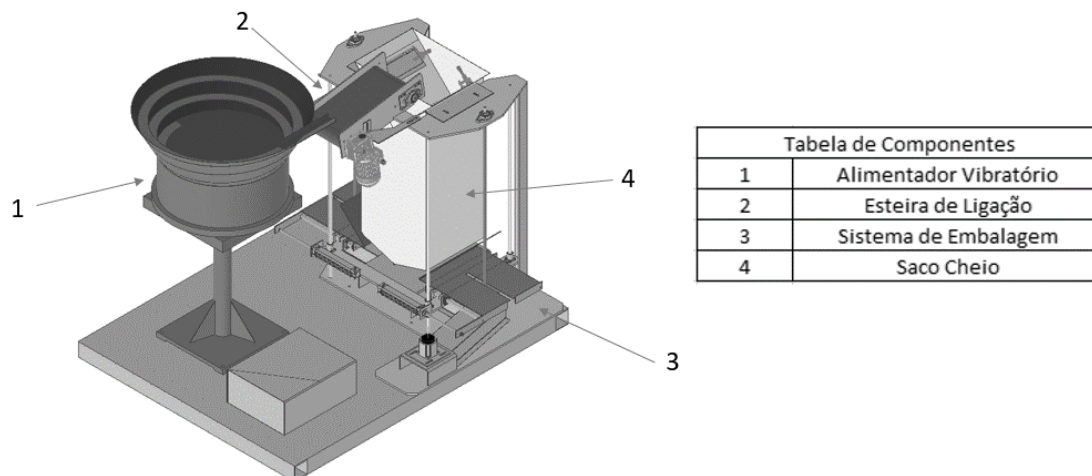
Representação CAD 3D da máquina de contagem de cabos automática com os componentes identificados
